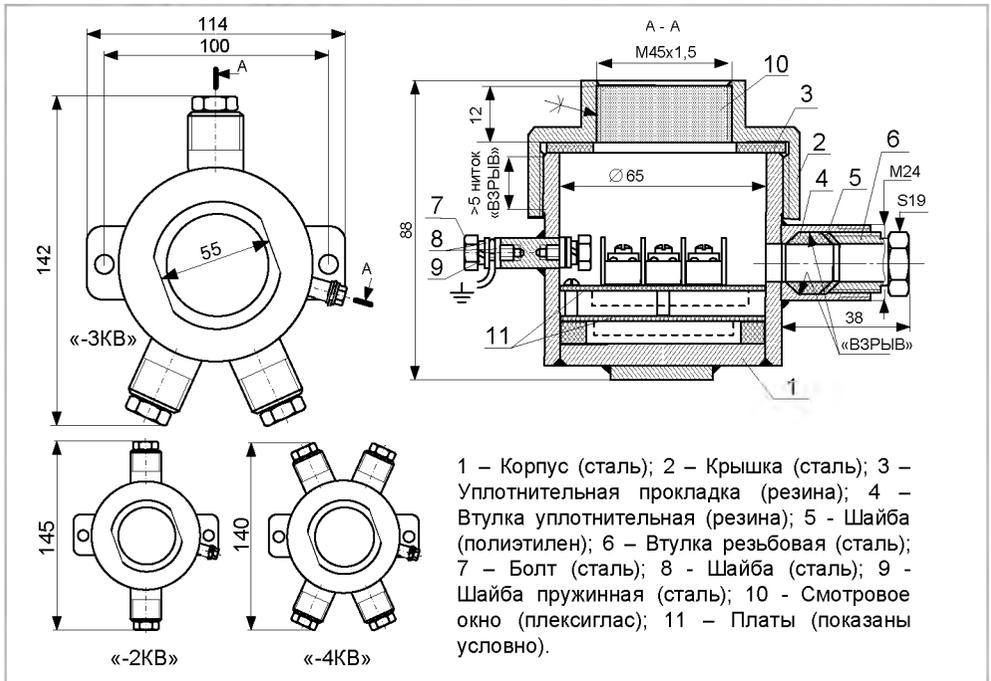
Внешний вид. Размеры. Чертеж средств взрывозащиты
